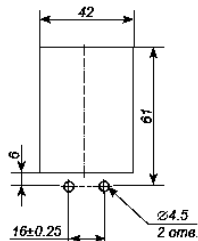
Габаритные и установочные размеры реле промежуточного РПУ-2М-202
